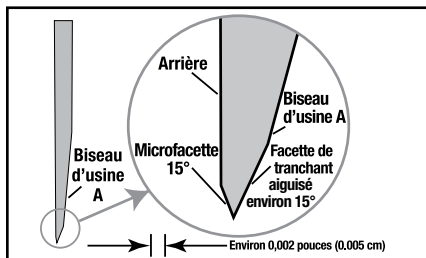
Coupe transversale du tranchant d'usine d'un couteau asiatique traditionnel typique grossi 50x (pour droitier).
